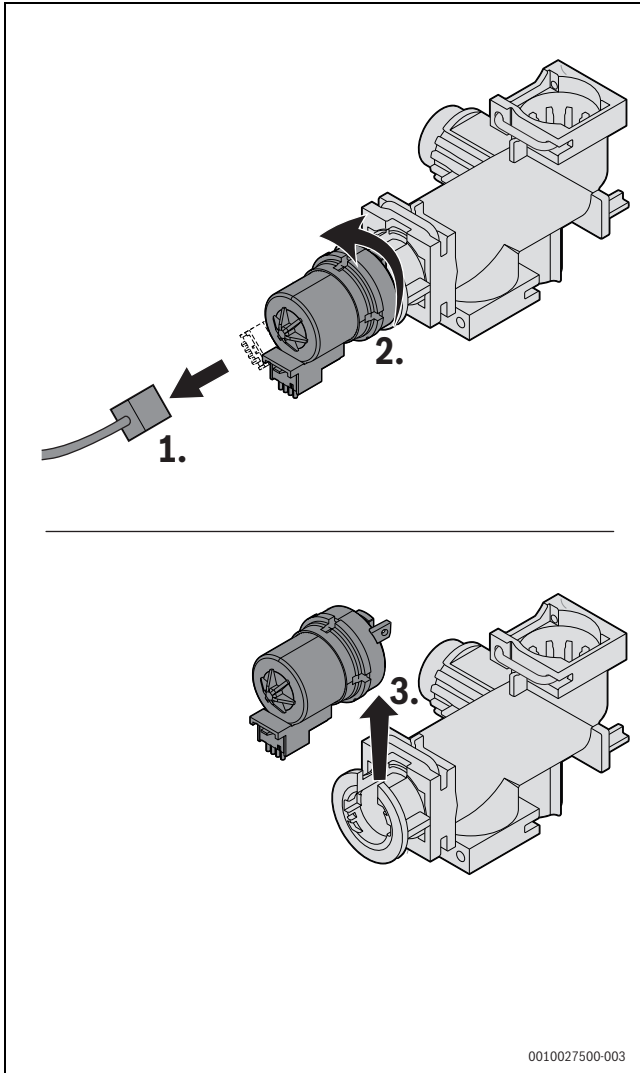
Motor am 3-Wege-Ventil ausbauen (Variante ohne Schrauben)
